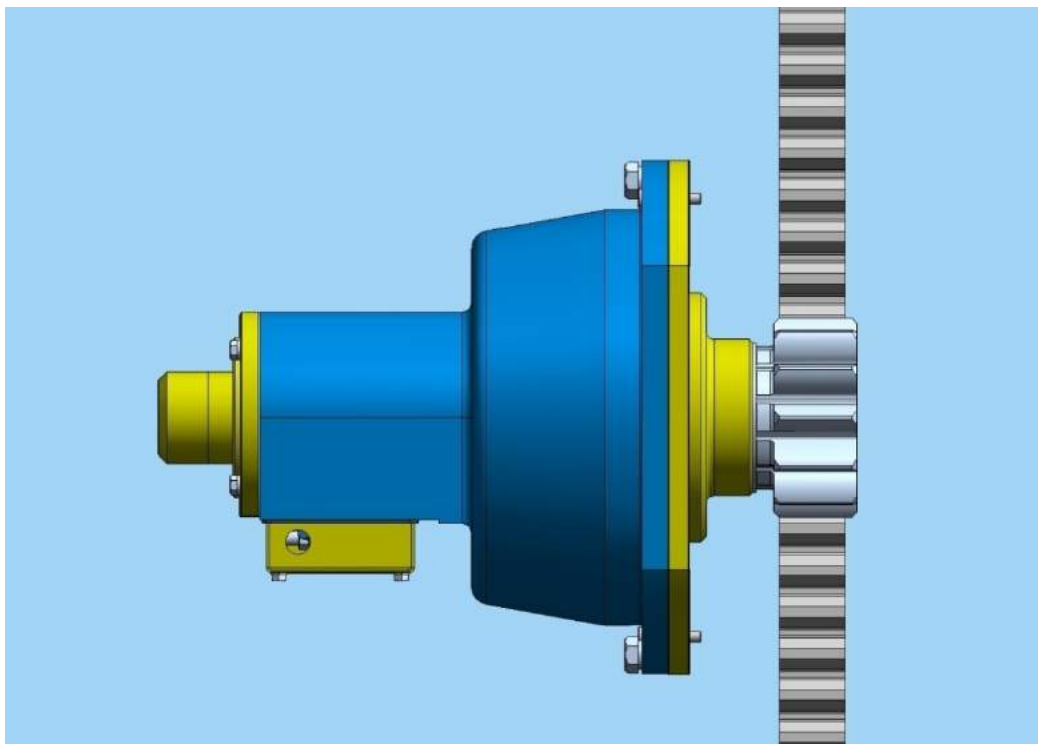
Montaje Piñón Cremallera Izquierda
